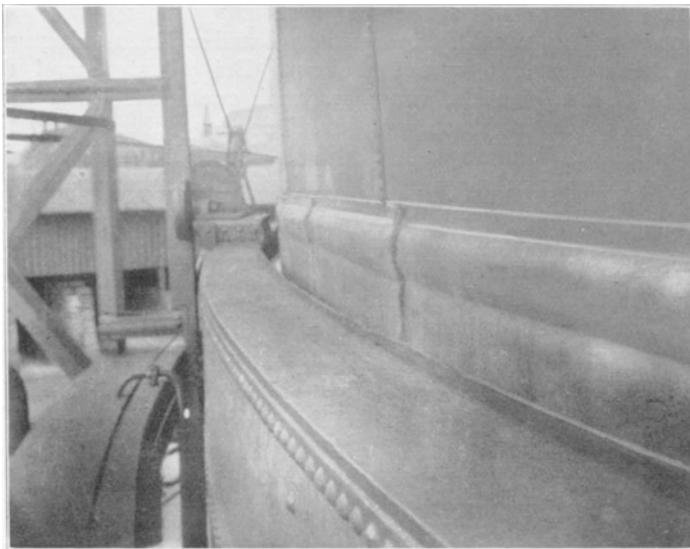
Durch Schweißung ausgebesserte Gasbehälterglocke.
